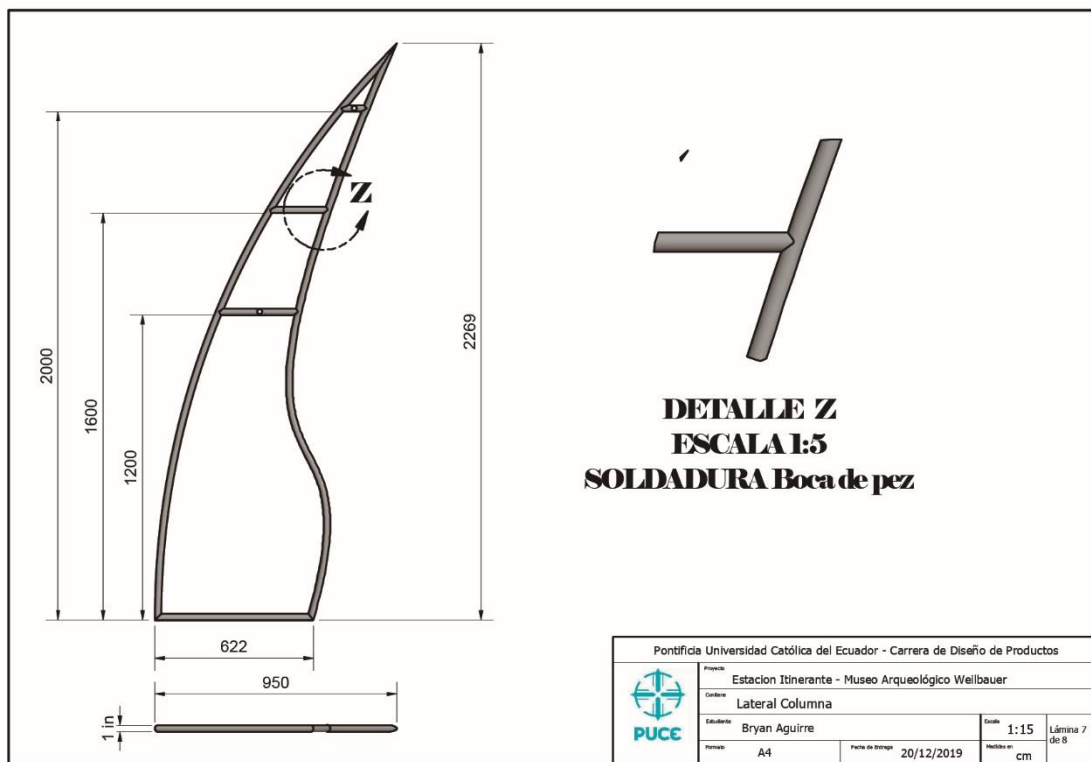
Detalle lateral de las Columnas. Fuente elaboración propia.
